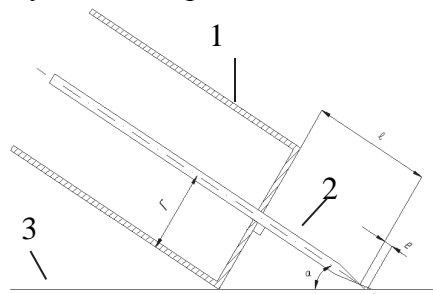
Расчетная схема для определения величин тактических параметров аргонодуговой сварки неплавящимся электродом
